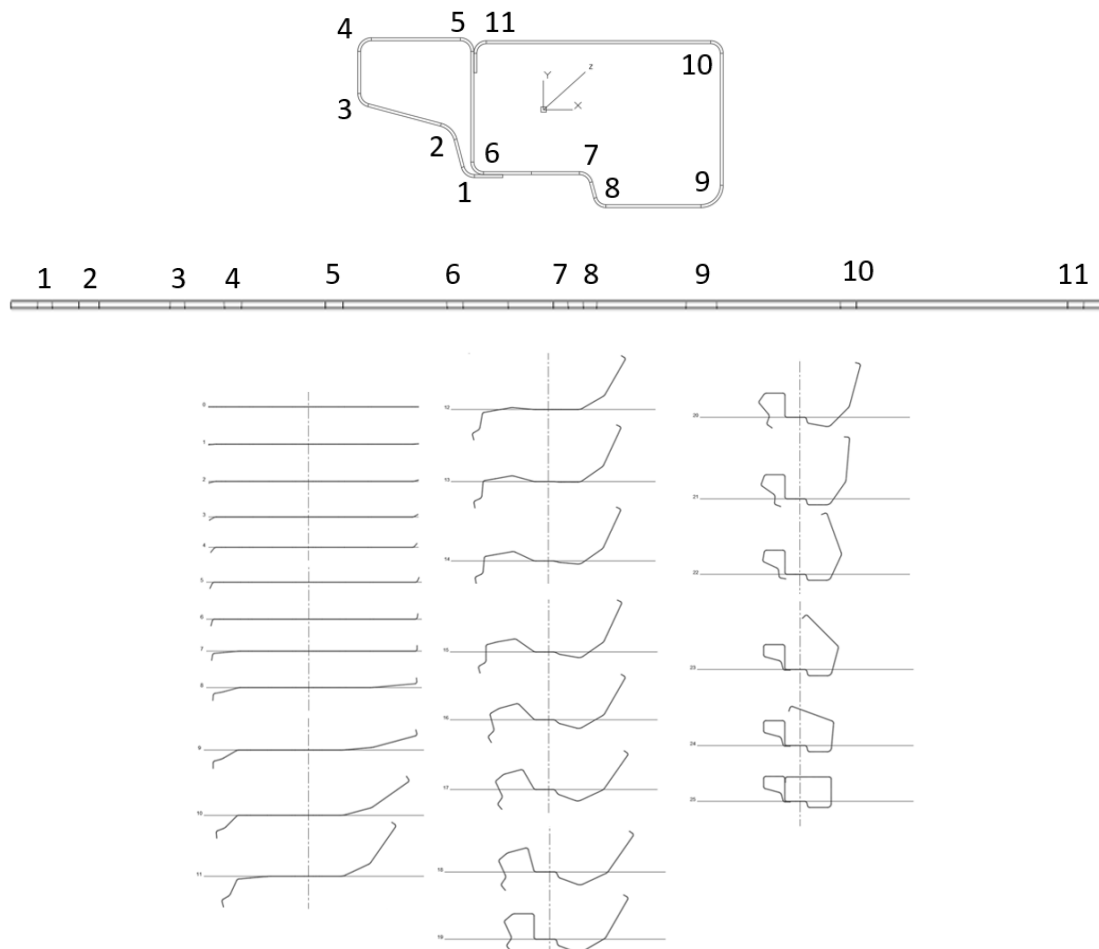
Сечение профиля бампера и места сварки
